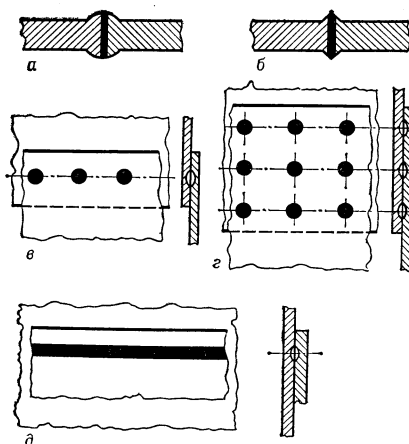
Виды сварных соединений и типы швов при контактной сварке: а — стыковое при сварке сопротивлением; б — стыковое при сварке плавлением; в — нахлесточное, выполненное однорядным точечным швом; г — нахлесточное, выполненное многорядным точечным швом; д — нахлесточное, выполненное однорядным роликовым швом.
